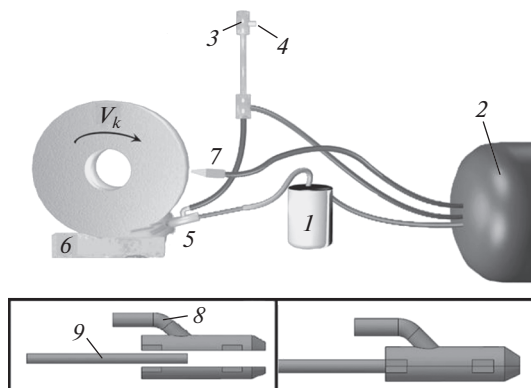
Схема экспериментальной установки: 1 – система подачи смазки *Spraymat 700*; 2 – компрессор; 3 – вихревая труба; 4 – выход горячего воздуха; 5 – сопло *SAMQL*; 6 – заготовка; 7 – сопло *WCJ*; 8 – подвод холодного воздуха; 9 – трубка подачи масла.
